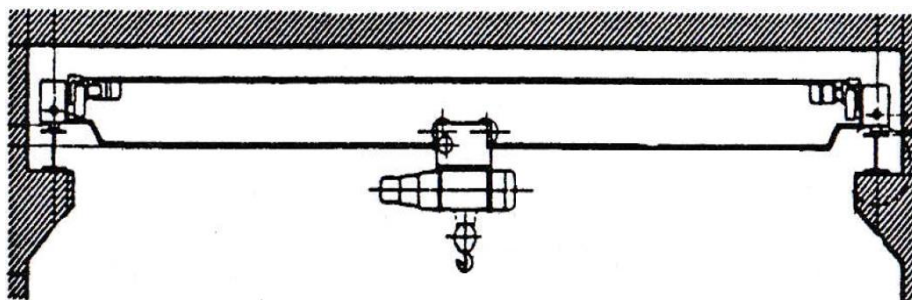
Viga principal de tipo cajón (10) (p. 258)
